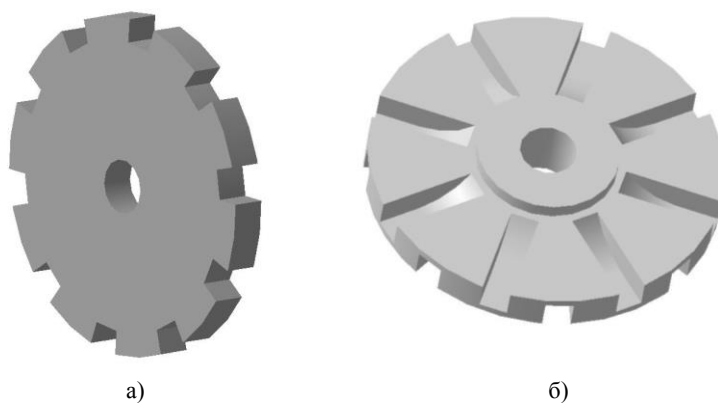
Шлифовальные круги с прерывистой рабочей поверхностью:
